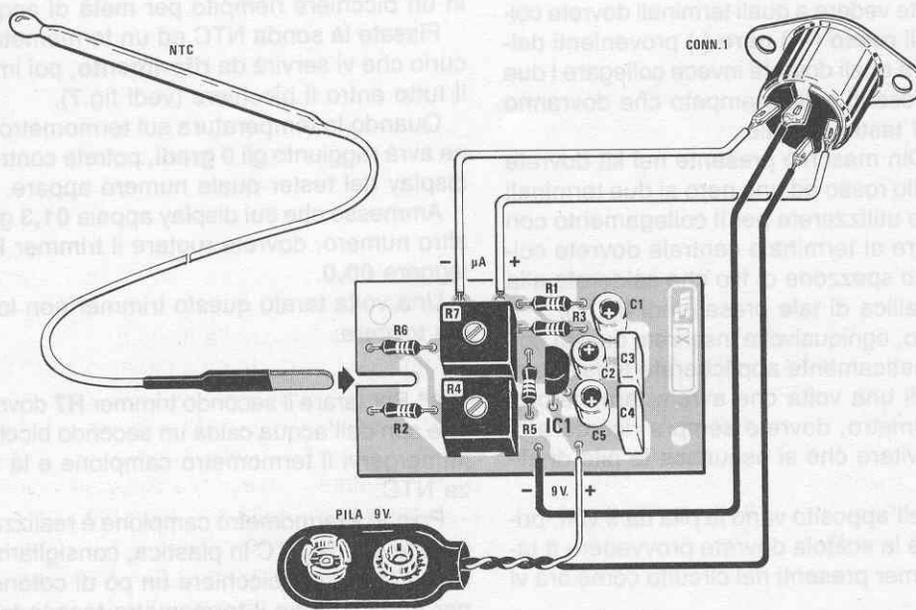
Schema pratico di montaggio. Si noti la fessura per l'innesto del connettore della NTC e le connessioni del CONN.1, che dovrete utilizzare per prelevare la tensione da applicare al Tester e come interruttore di rete (vedi fig.6).
